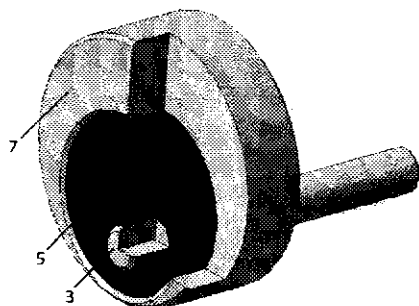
Исполнительный механизм предлагаемой системы
